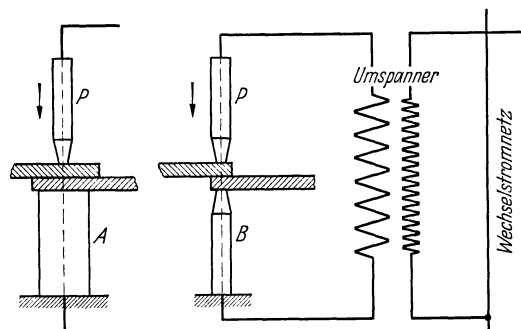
Grundform der elektrischen Punktschweißung.
